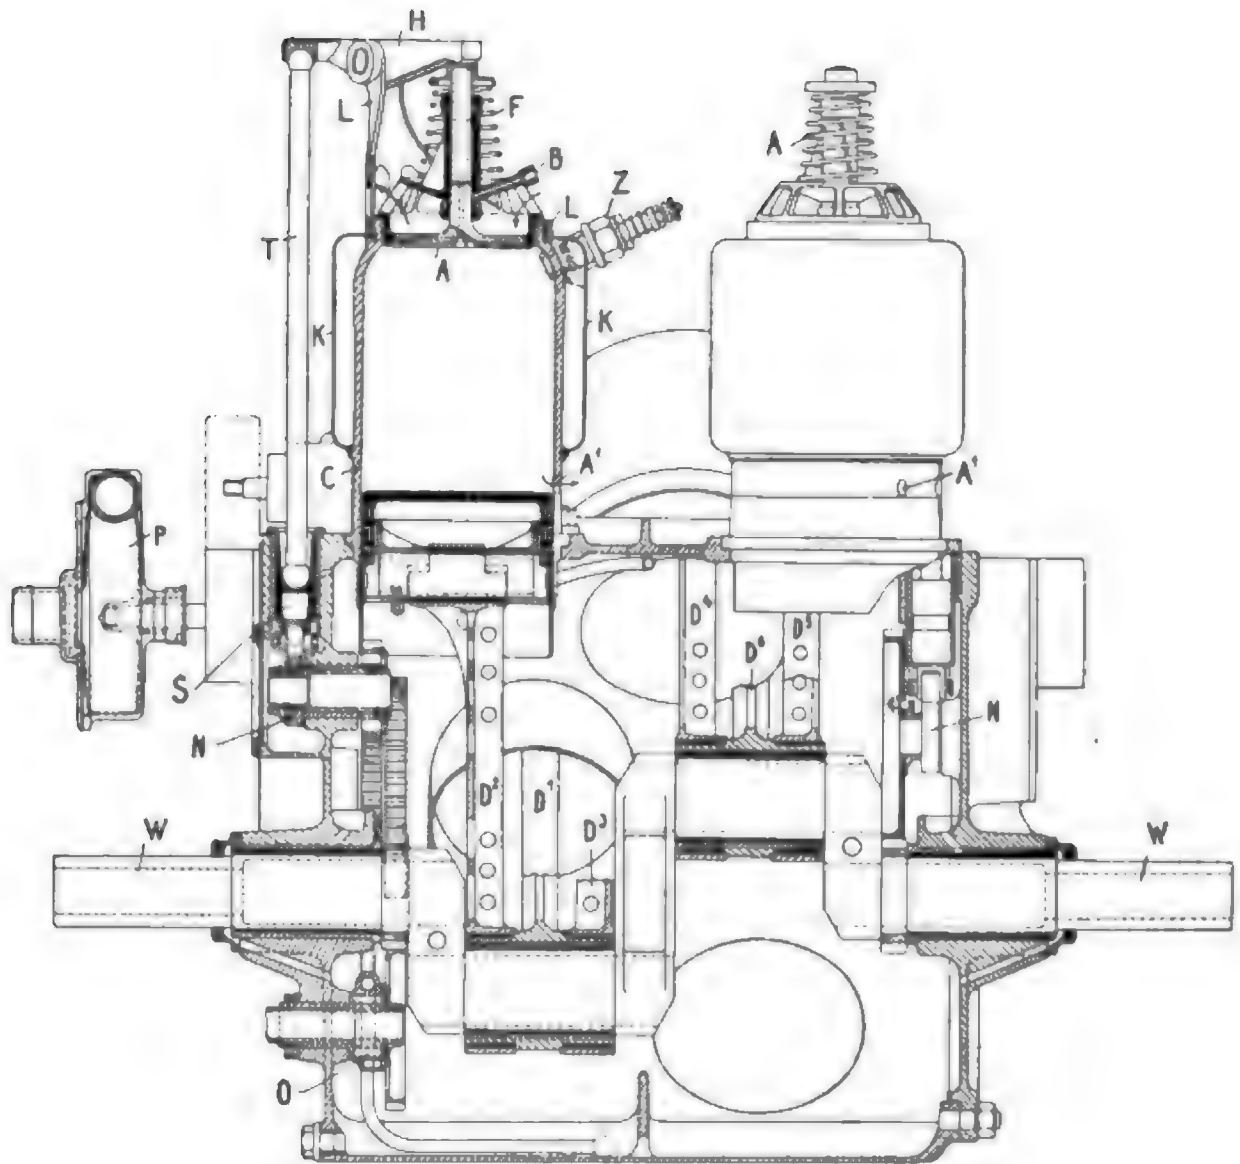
Zeichnung des Flugmotors von Dr. Huth. Längsschnitt.
